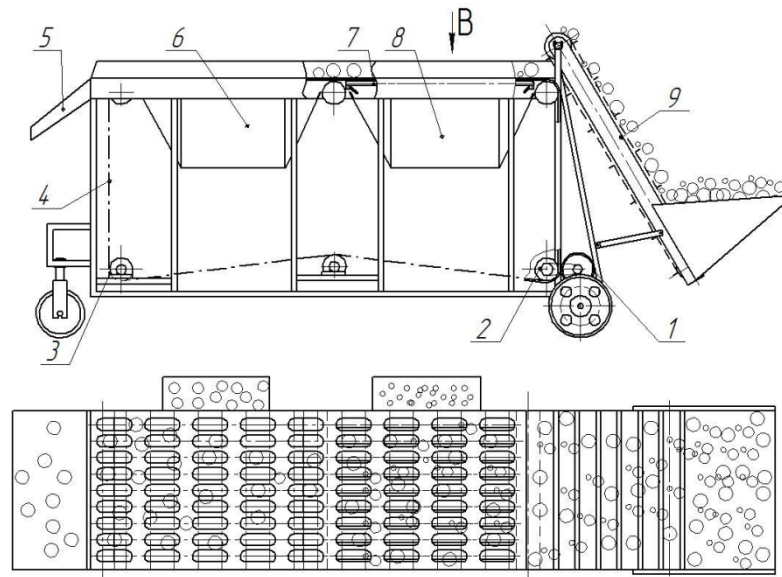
Схема запропонованої конструкції, з новим робочим органом транспортерного типу: 1 – приводний мотор-редуктор; 2 – ведучий барабан; 3 – підтримувальний барабан; 4 – транспортерна стрічка; 5 – лоток приймання великої фракції; 6 – лоток приймання середньої фракції; 7 – калібрувальне решето; 8 – лоток приймання дрібної фракції; 9 – транспортер для подачі з приймальним лотком [2].
